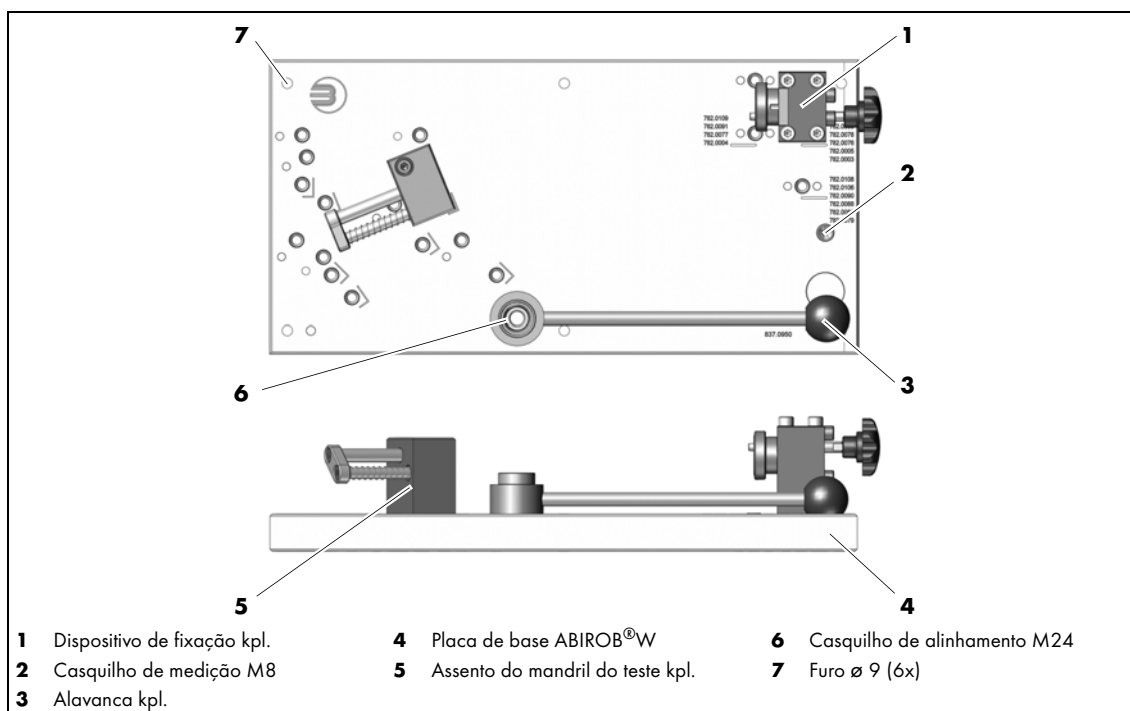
Instalar o dispositivo de ajuste ABIROB®W
